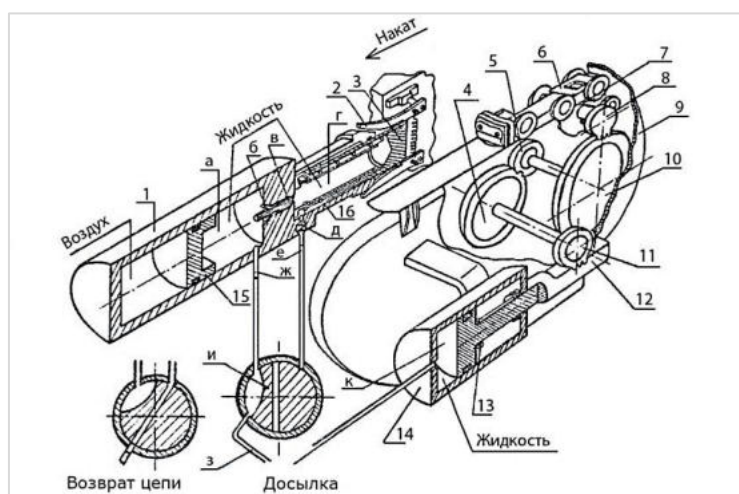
Схема досылателя пушки 2А36 «Гиацинт-Б». 1 – цилиндр; 2 – кулачок; 3 – шток; 4 – вал-шестерня; 5 – шестерня; 6 – цепь; 7 – звёздочка; 8 – вал-шестерня; 9 – корпус; 10 – вал-шестерня; 11 – шестерня; 12 – шток-рейка с поршнем; 13 – комплект пружин; 14 – гидроцилиндр исполнительный; 15 – поршень; 16 – комплект пружин; *а* – полость высокого давления гидропневматического аккумулятора; *б* – каналы; *в* – запорный клапан; *г* – полость низкого давления жидкости; *д* – обратный клапан; *е*, *ж*, *з* – трубопроводы; *и* – кран управления; *к* – поршневая полость исполнительного цилиндра
